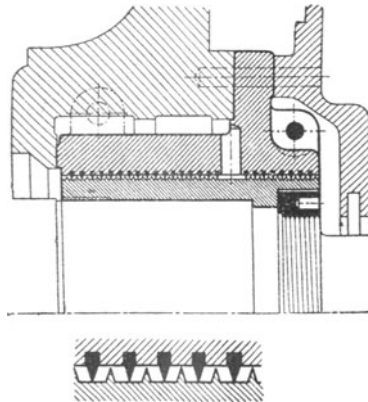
Querschnitt der Labyrinthdichtung einer Dampfturbinenwelle.
